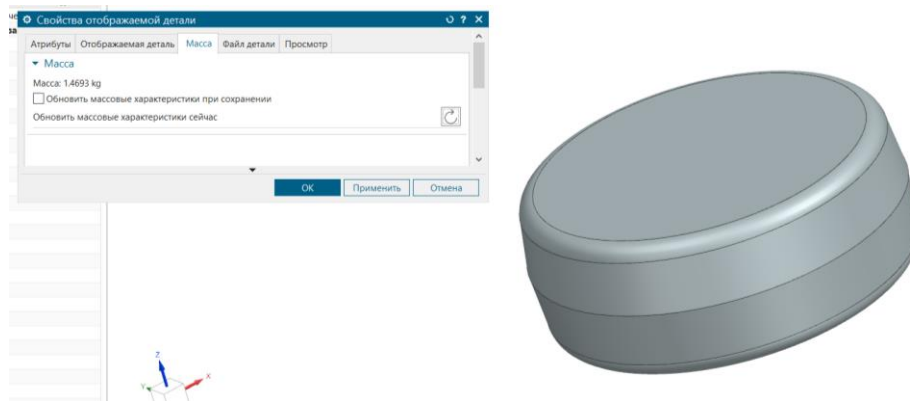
3D-модель заготовки, що отримується на молоті
